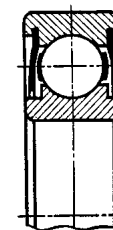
Подшипник шариковый радиальный однорядный с двумя защитными шайбами
